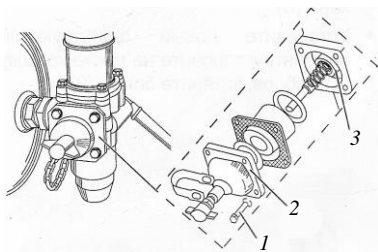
Очистка фильтрующего элемента регулятора давления пневмосистемы: 1 – болт; 2 – крышка; 3 – фильтрующий элемент
